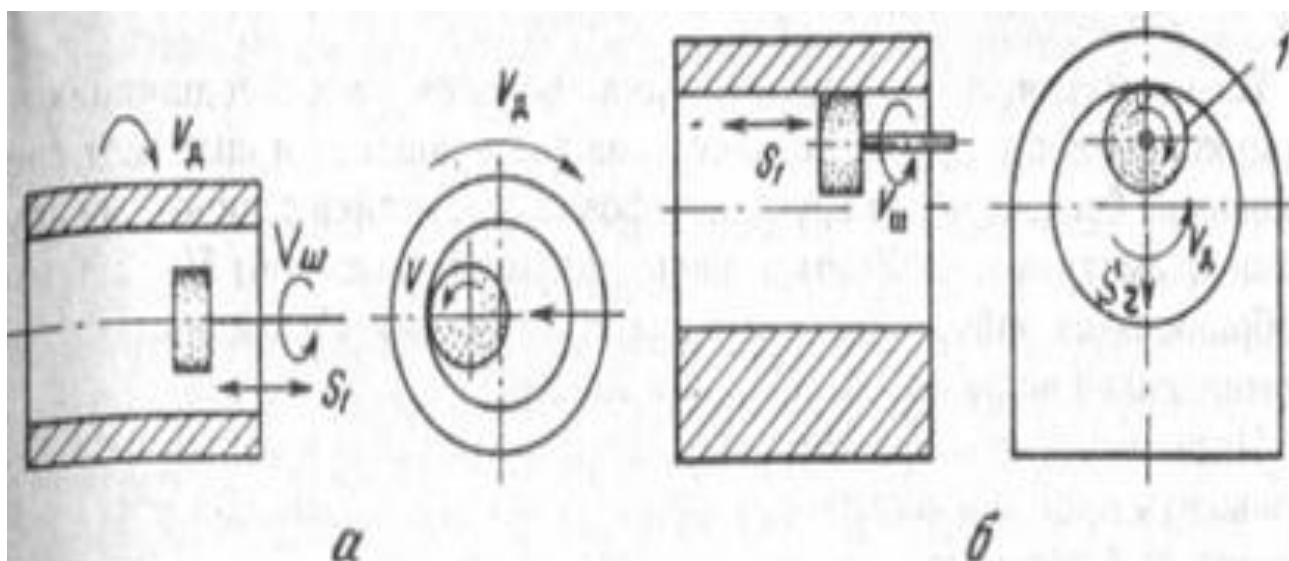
Схемы внутреннего шлифования: а – при вращающейся заготовке, б – при неподвижной заготовке.
